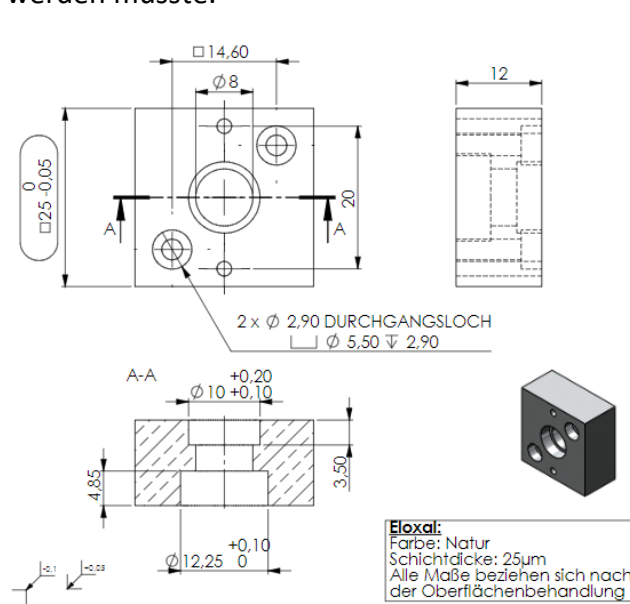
Technische Zeichnung von Aluminiumadapters
